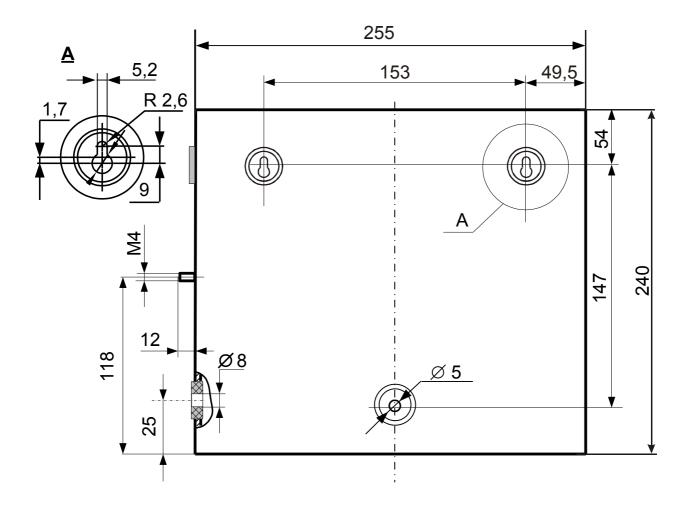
Габаритные и присоединительные размеры БЦП в корпусе ИБП-12
